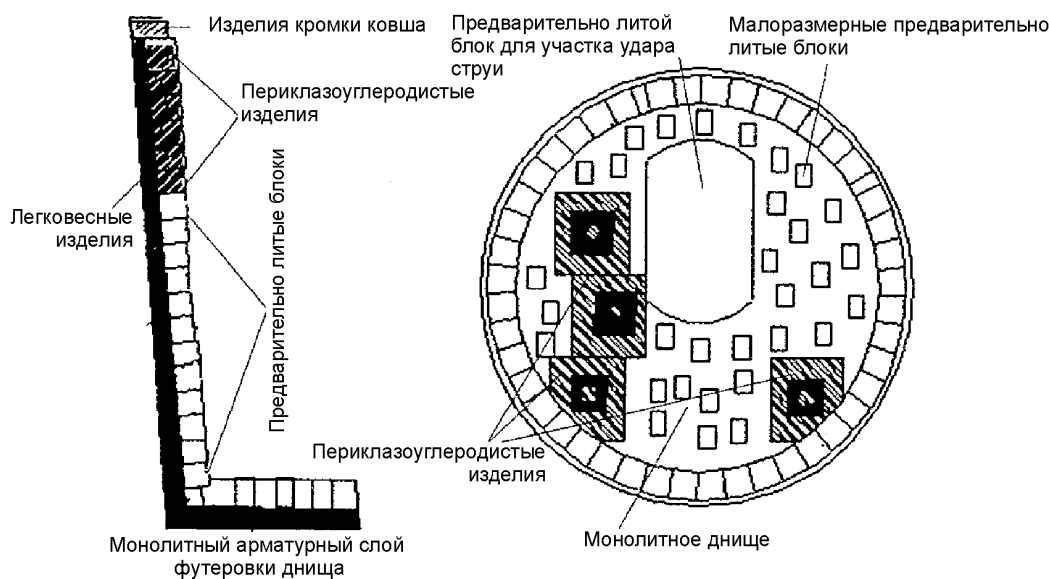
Сталеразливочный ковш с футеровкой из предварительно литых блоков
